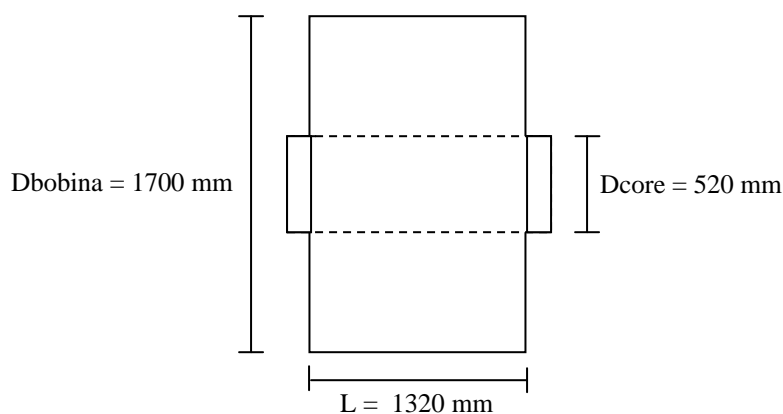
Dimensiones máximas y mínimas de las Bobinas de Aluminio
